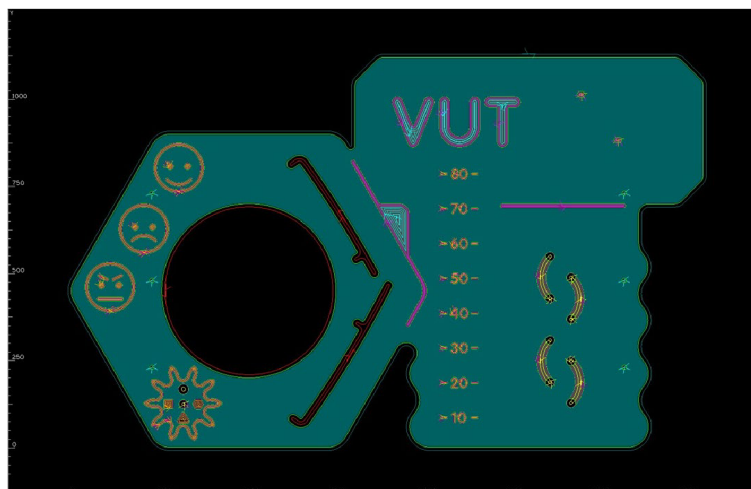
Zobrazení geometrií horní strany a přidané operace pro obrábění
